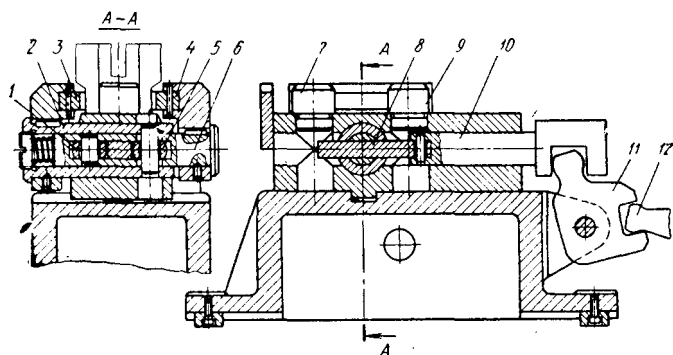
Двухместное приспособление для фрезерования впадин полумуфт
